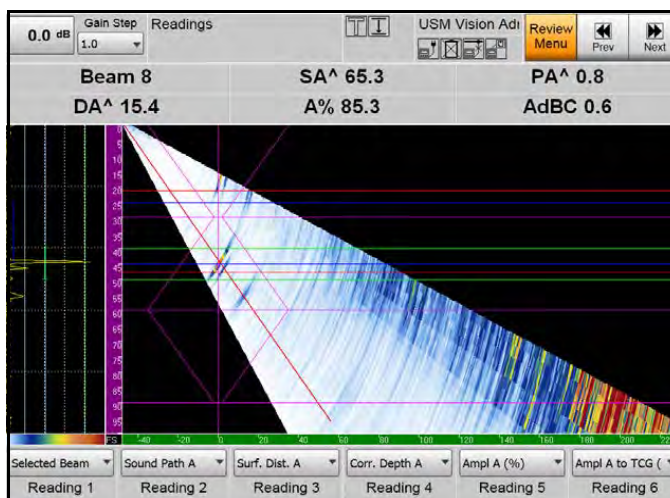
Контроль V-образного сварного шва 30 мм
